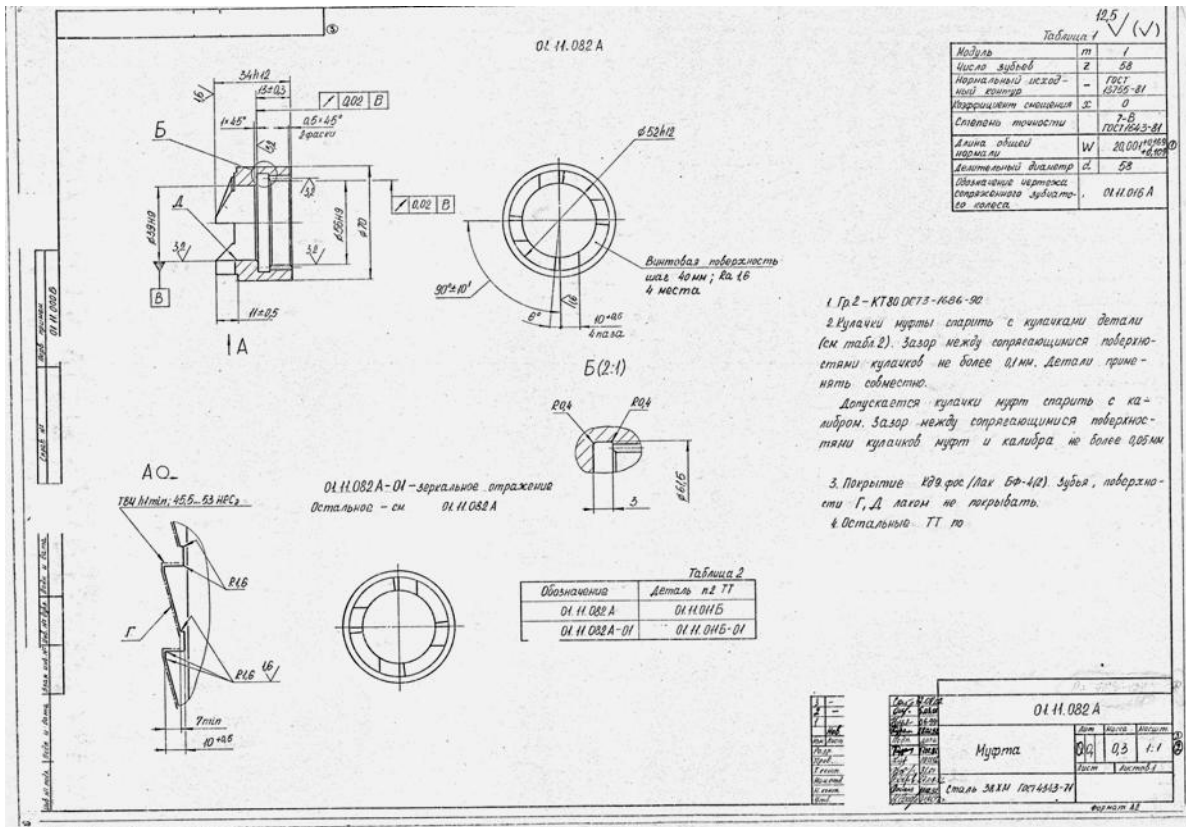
Технический многовидовый чертёж детали «Муфта»
